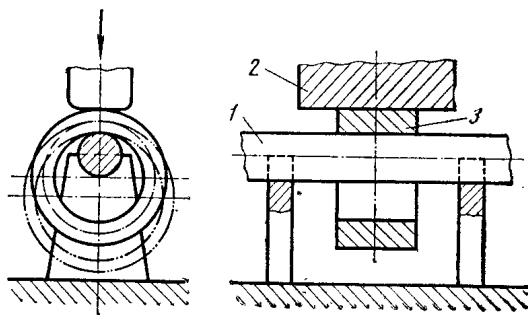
Схема раскатки прошитой заготовки на дорне:
